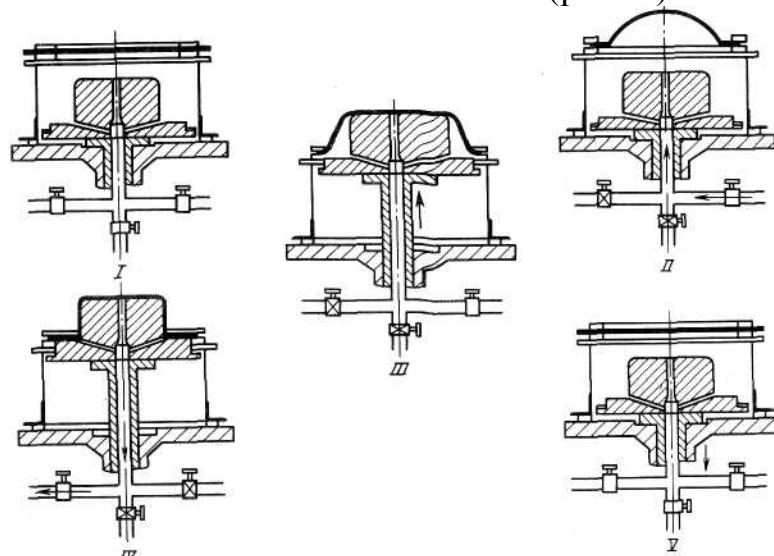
Схема позитивной формовки с предварительной пневматической вытяжкой
